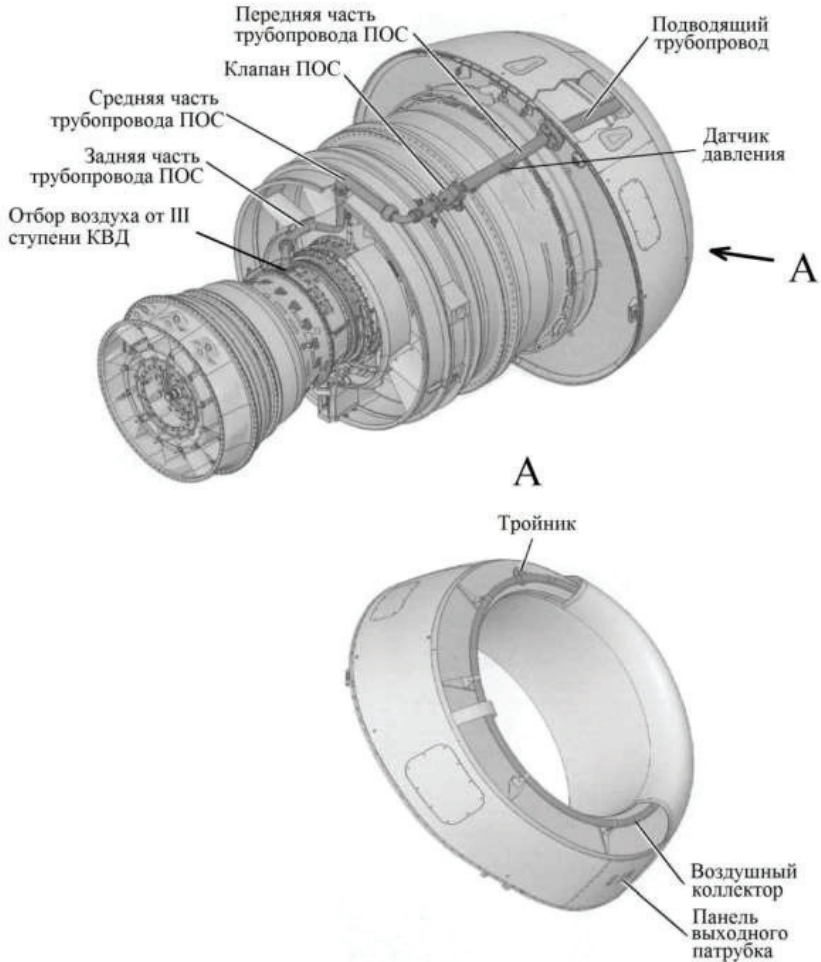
ПОС воздухозаборника двигателя самолета Суперджет
